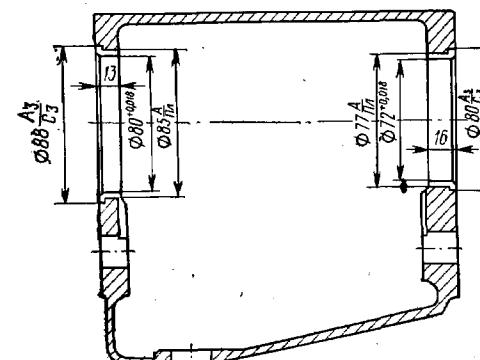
Размеры отверстий и ремонтных колец при восстановлении отверстий под подшипники в картере коробки передач
